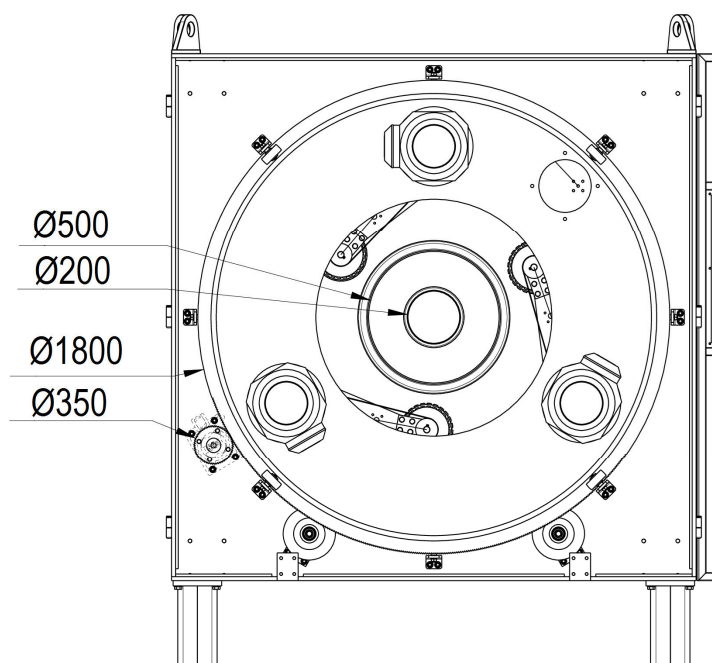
Dimensões do carreto de servomotor, prato rotativo e tubos a cortar
